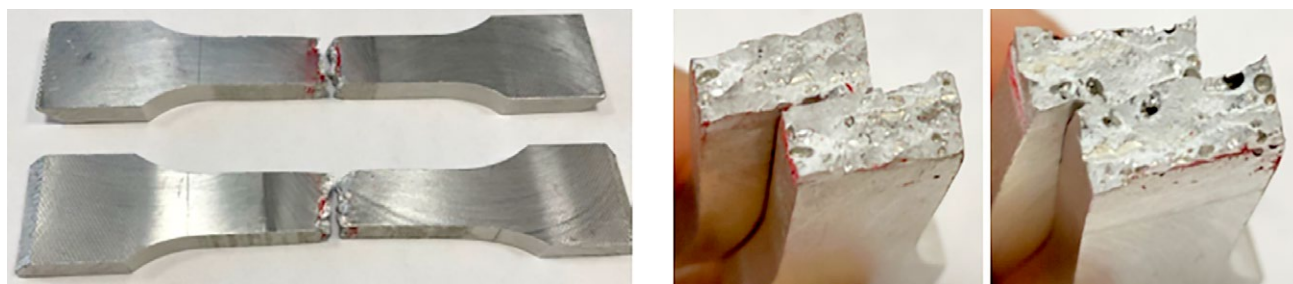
Разорванные образцы из напечатанного алюминия, сваренного с 6082Т4.
